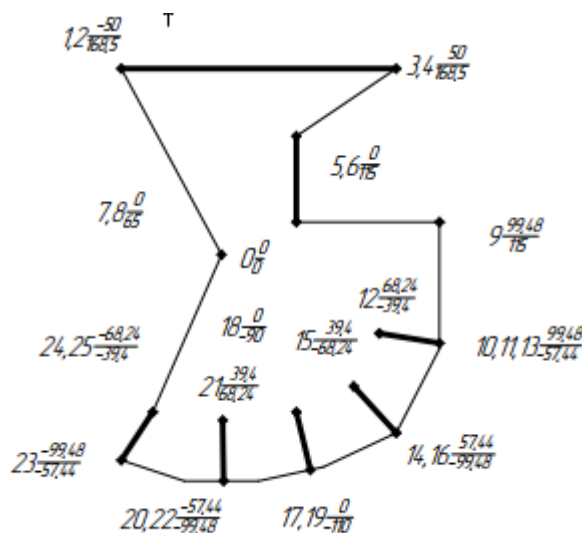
Траєкторія руху ріжучого інструменту №2 на операції 055 фрезерній з ЧПК
